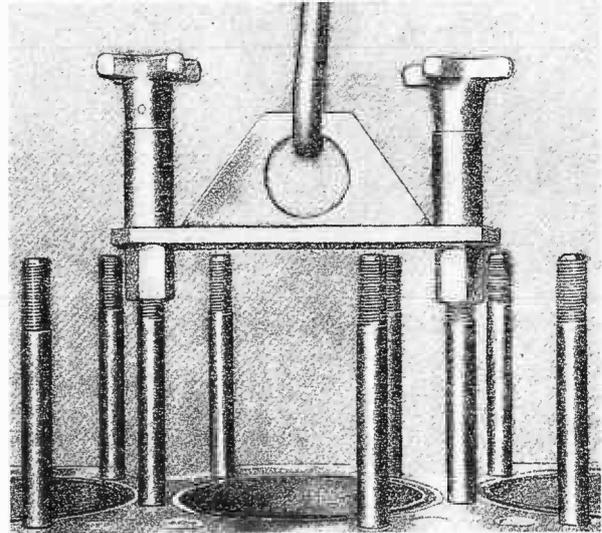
Zylinderblock mit Vorrichtung und Hebezeug aufsetzen
